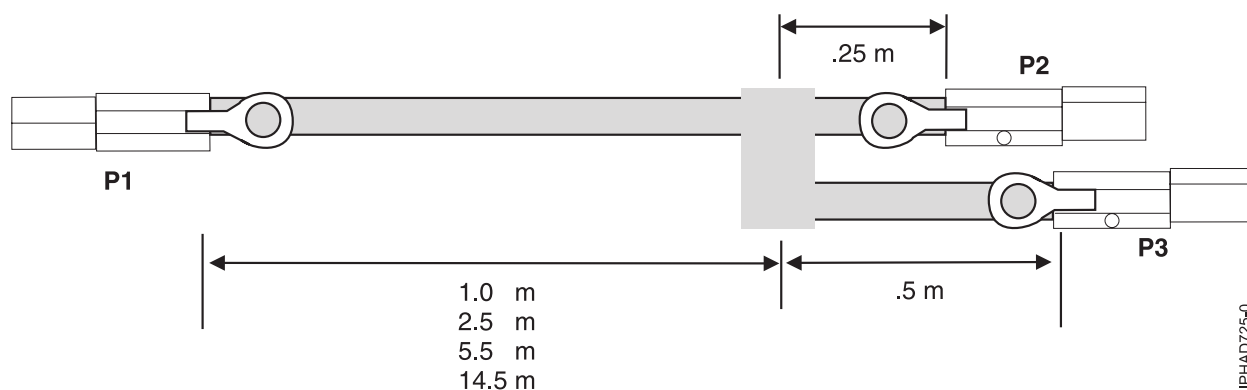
Comprimentos de cabo de montagem de cabo YO externo SAS
